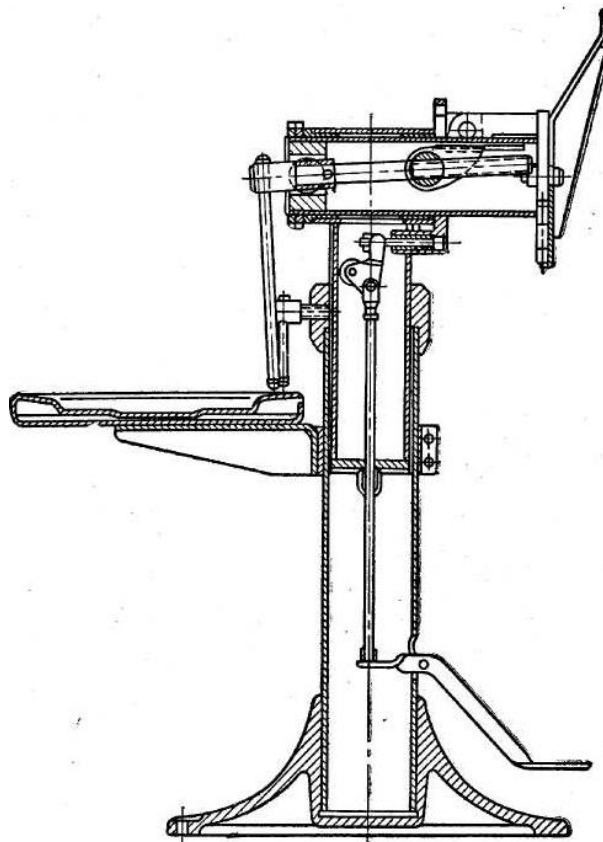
Кінематична схема станду з передачею гвинт-гайка.
